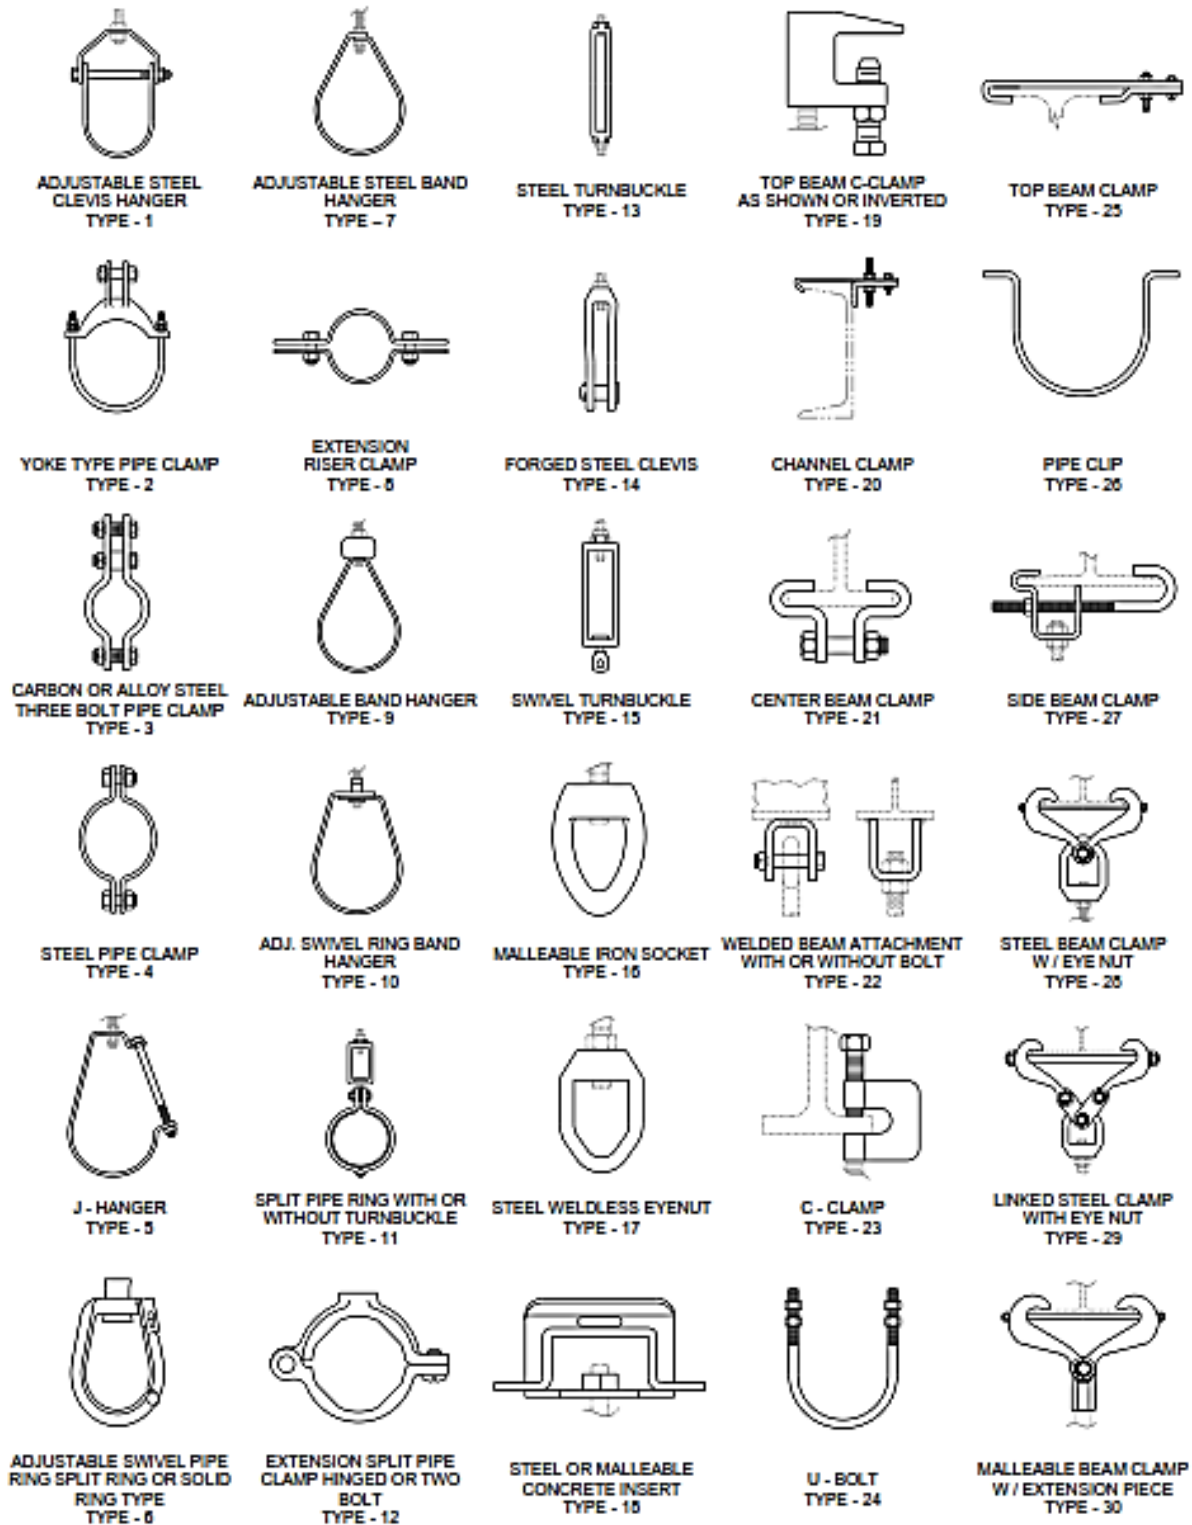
Tipos de soporte para tubería (1 – 30) (Manufacturers Standardization Society of the Valve and Fittings Industry. INC [MSS], 2009)
